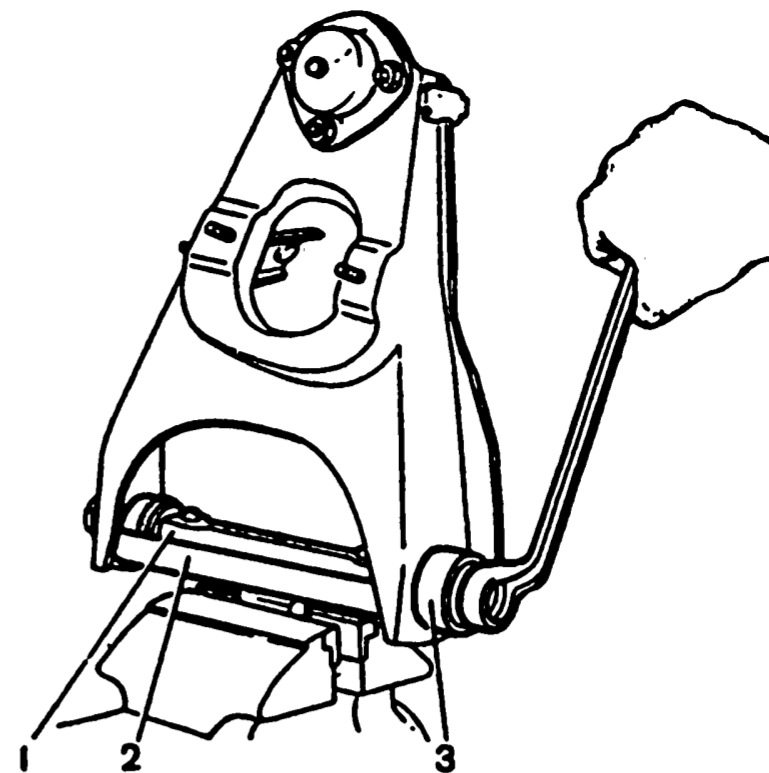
Запрессовка шарниров нижнего рычага: 1 - ось рычага; 2 - приспособление А.74177/2; 3 - приспособление А.74177/1
